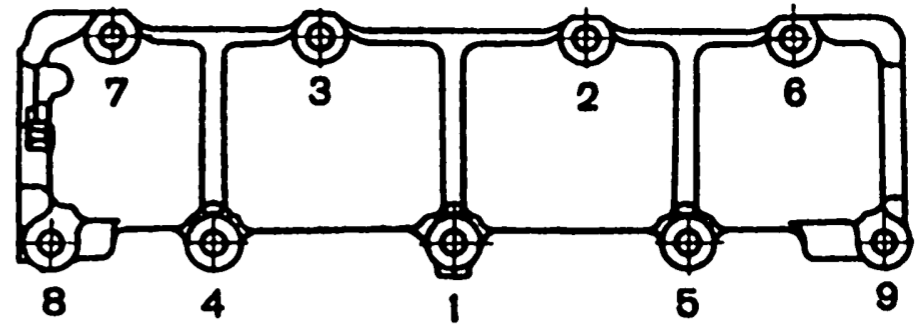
Порядок затягивания гаек корпуса подшипников распределительного вала
